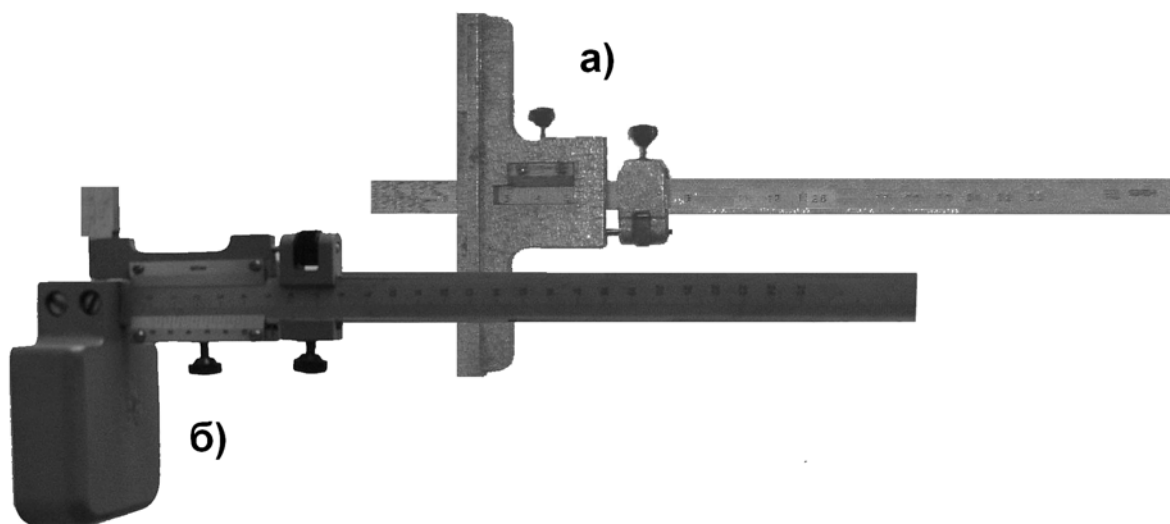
Конструкція штангенглибиноміра а) і штангенрейсмуса б).
